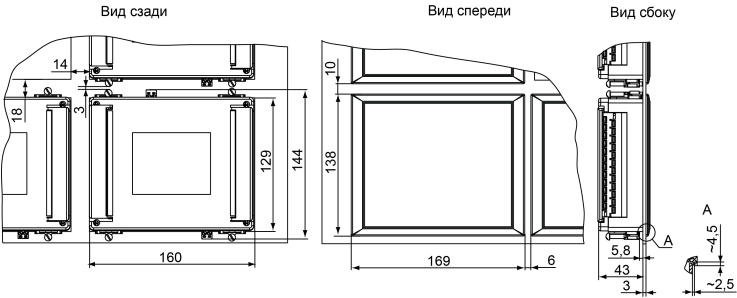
Прибор в корпусе Щ7, установленный в щит толщиной 3 мм
